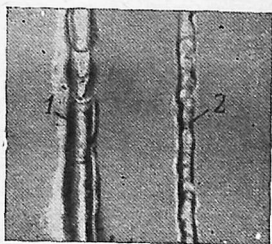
Гелиево-дуговая сварка меди.
